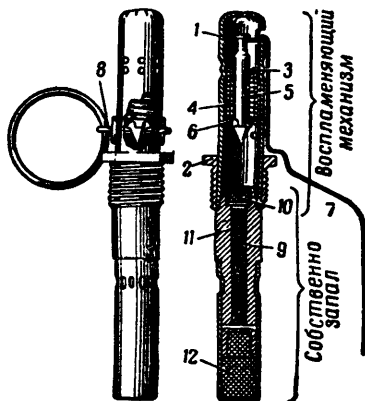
Внешний вид и вид в разрезе запала УЗРГ:
